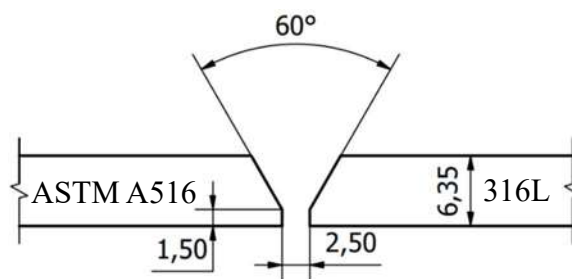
Diseño y dimensiones (mm) de la junta disímil.
